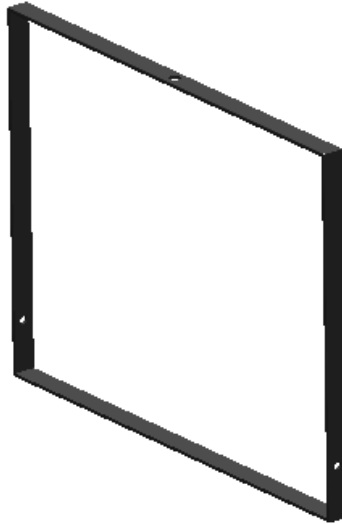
Estructura de sujeción. Fuente: Elaboración propia
